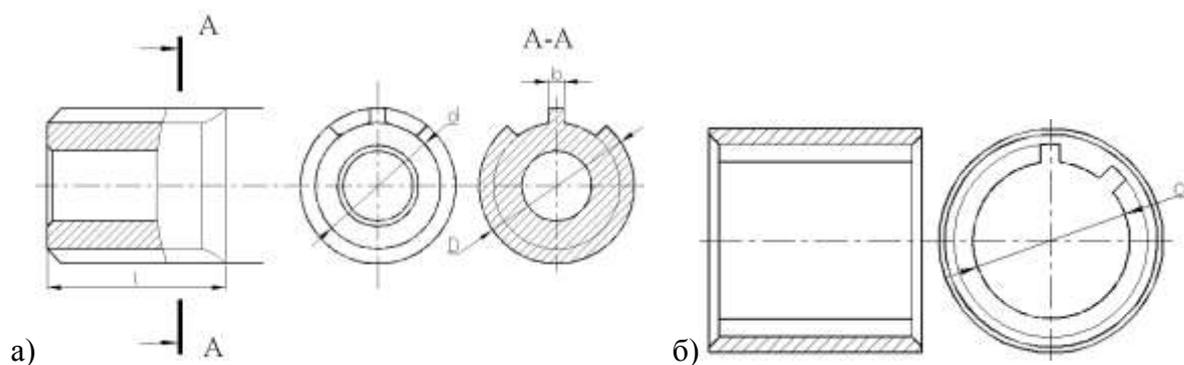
Детали со шлицами: а) условное изображение шлицевого вала; б) условное изображение шлицевой втулки
